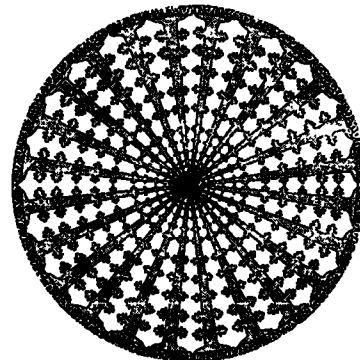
Схема теплофизической модели затвердевания цилиндрической и шаровой отливок при сужении фронта затвердевания в осевой зоне
